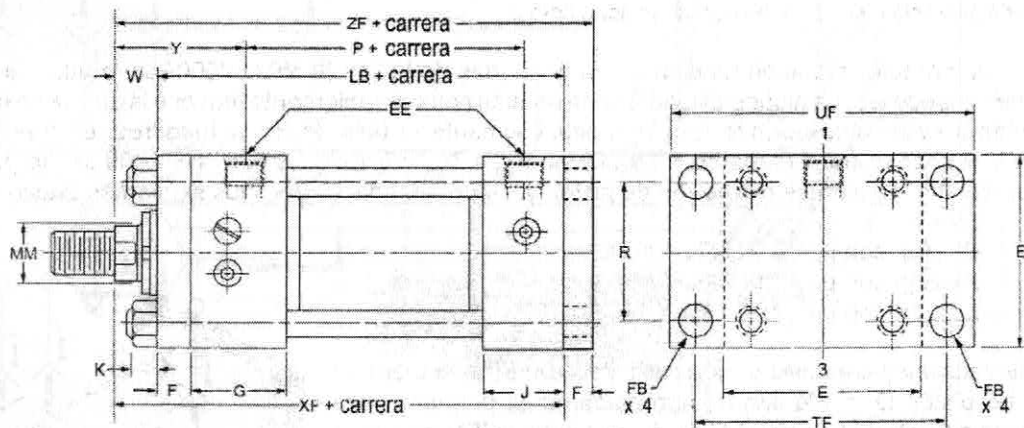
Dimensiones del actuador con montaje MX2 de la NFPA.
